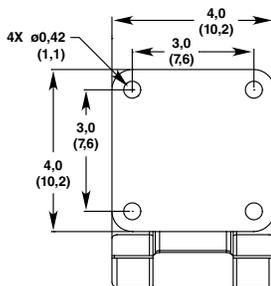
Q9033 Montagearm ohne Abmessungen der Manschettenbaugruppe in Zoll (cm)
